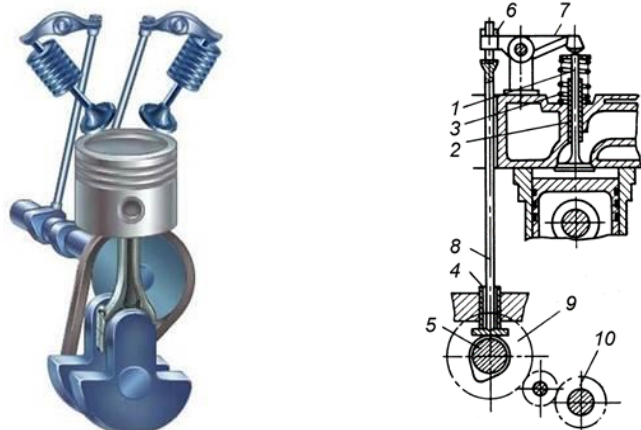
ГРМ з верхнім розташуванням клапанів: 1 – клапан; 2 – напрямна втулка; 3 – пружина; 4 – штовхач; 5 – кулачок розподільного валу; 6 – регулювальний гвинт; 7 – натискний важіль (коромисло); 8 – штанга; 9 – шестерня розподільного валу; 10 – шестерня колінчастого валу
